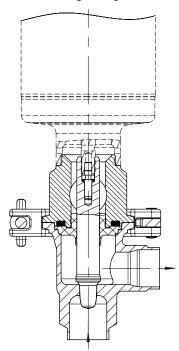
Stellventil Typ 3347/3379 mit Anschweißenden -Gussausführung
